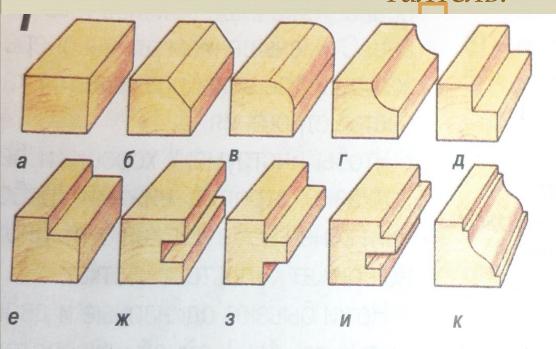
Профили струганых деталей: а — прямой; б — фаска; в — овал; г — галтель; д — четверть; е — фальц; ж — паз; з — гребень; и — паз-гребень; к — калевка.
